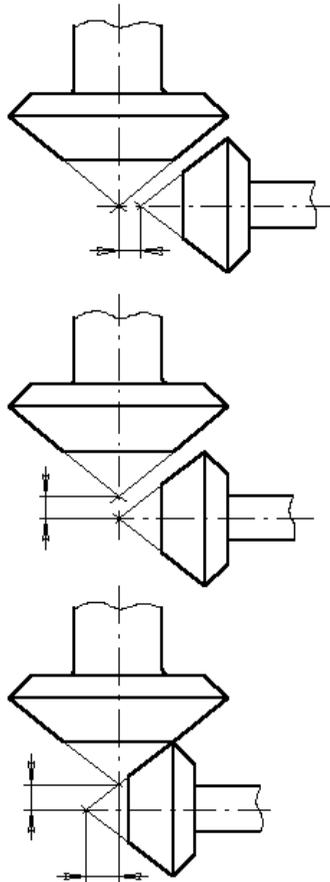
Несовпадение вершин делительных конусов конических зубчатых колес при сборке передач
